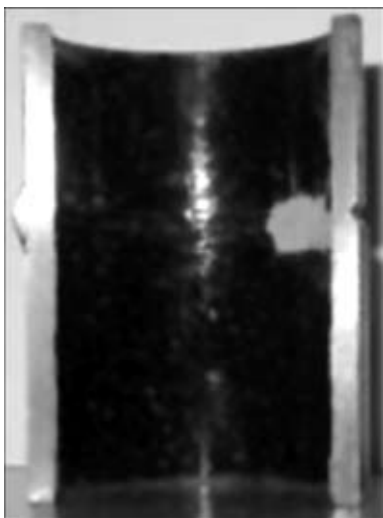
Стык эмалированных труб, выполненный импульсно-дуговой сваркой по слою эмали
